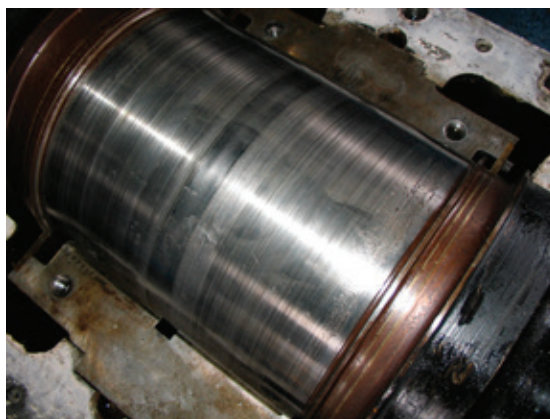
Коррозионное повреждение поверхности подшипниковой шейки вала ротора центробежного компрессора (материал — сталь 40ХН2МА)
